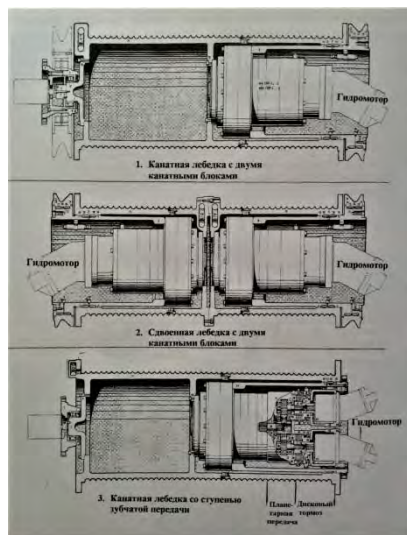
Гидравлический привод механизма подъема груза с планетарным редуктором и барабаном лебёдки
